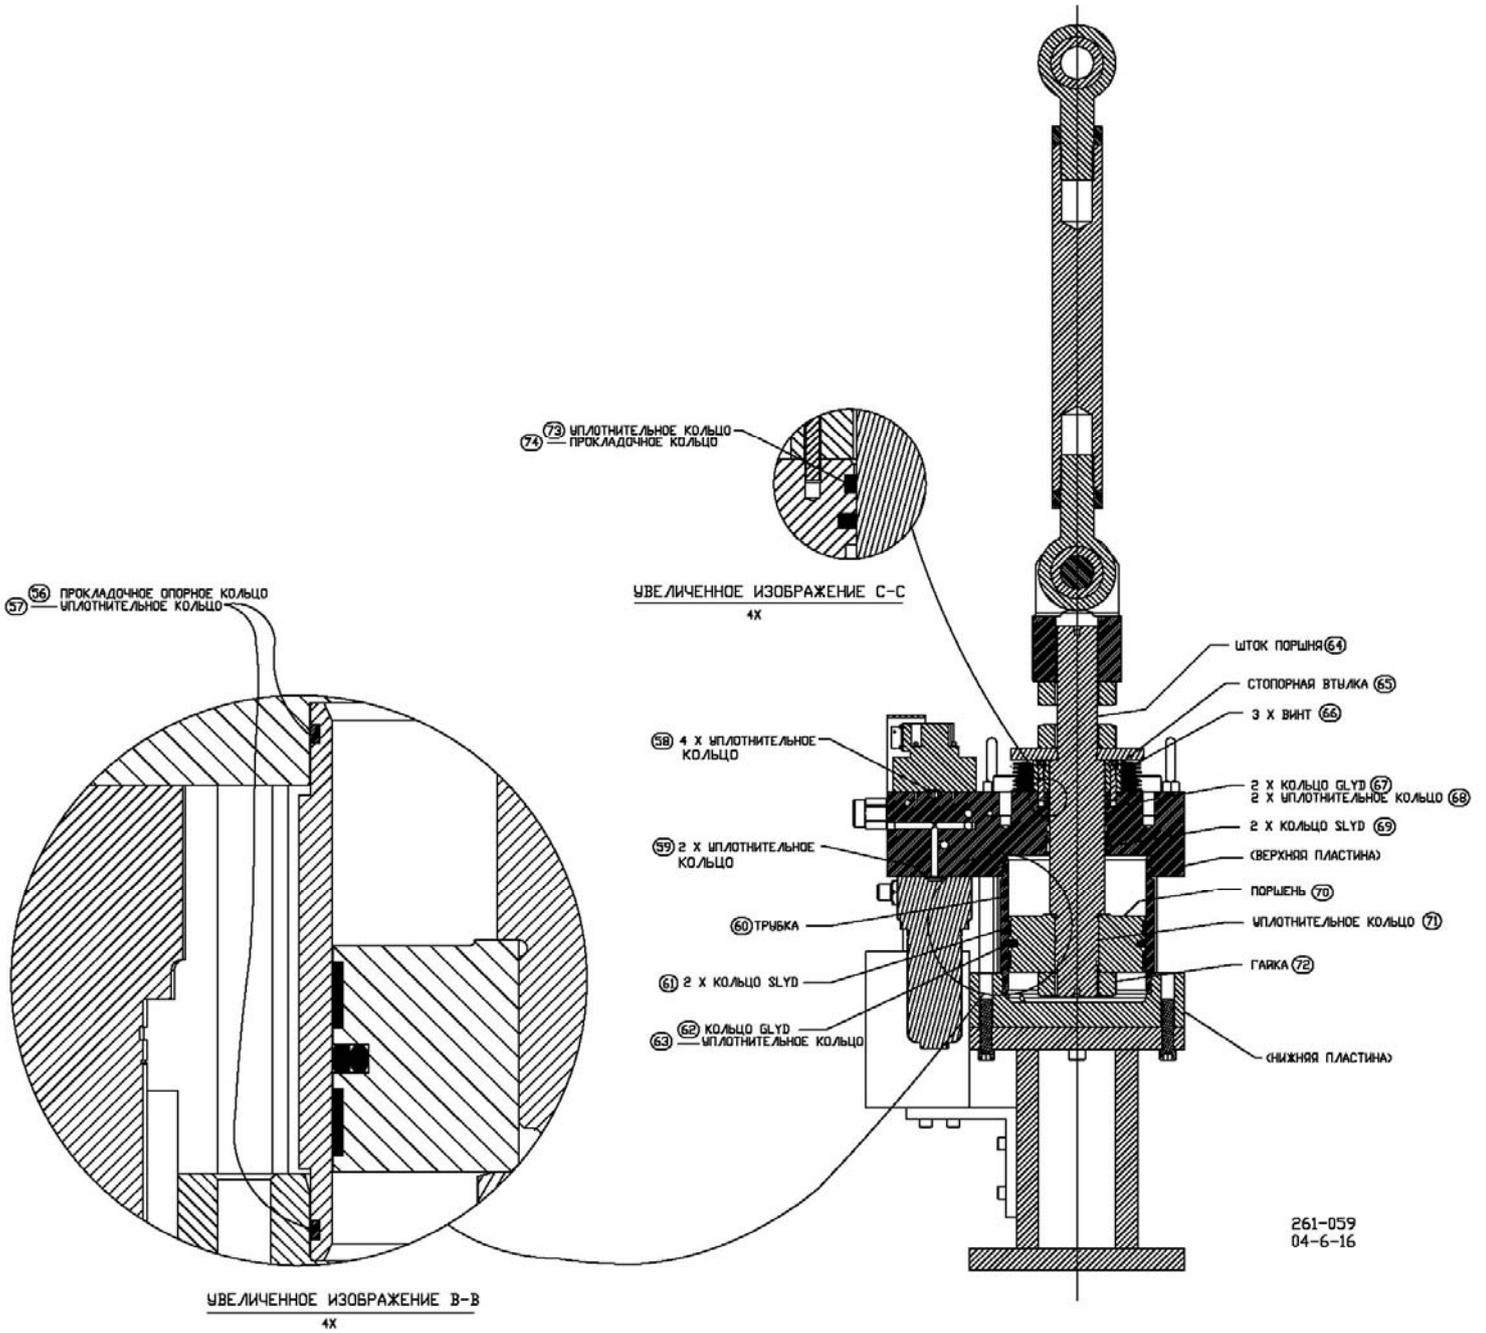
г. Привод IGV (неполный разрез с номерами по каталогу)
